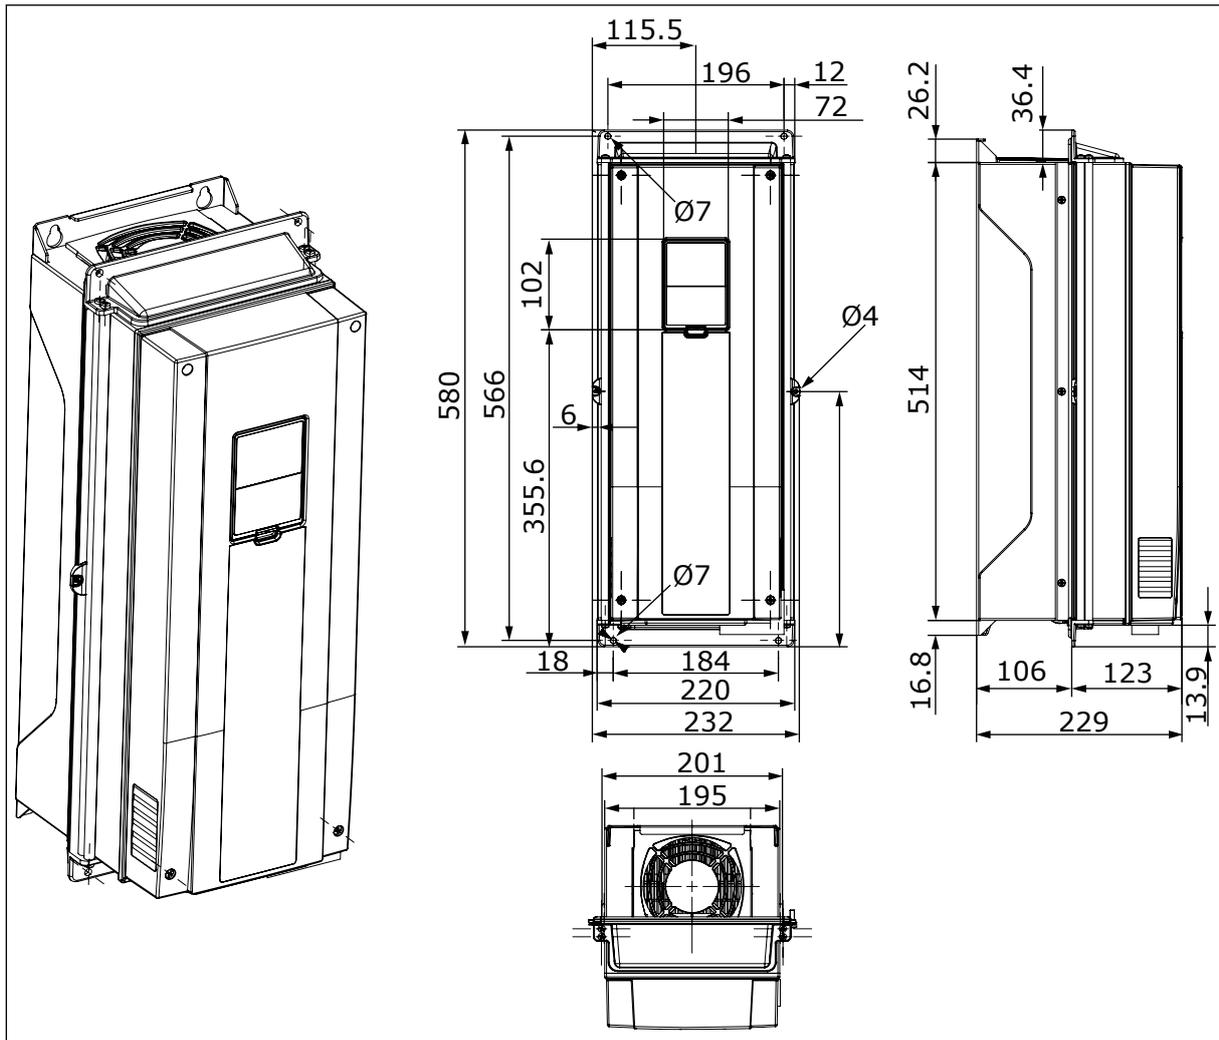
Abmessungen des Frequenzumrichters, Flanschbefestigung, MR6 [mm]
